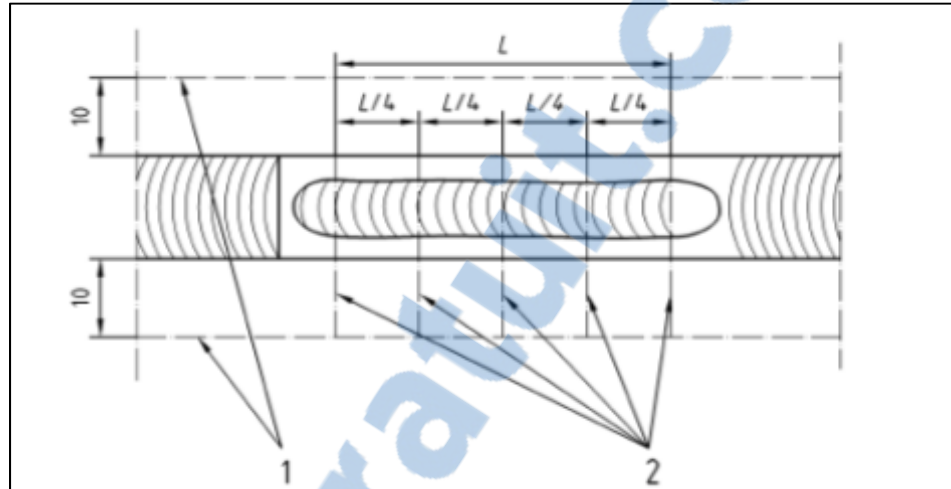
Position des coupes pour l'inspection des soudures déposées sur une éprouvette Tekken. Tirée de (International Standard, 2005)
